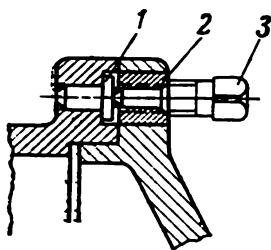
Extracteur d'un couvercle monté par ajustement avec serrage :
